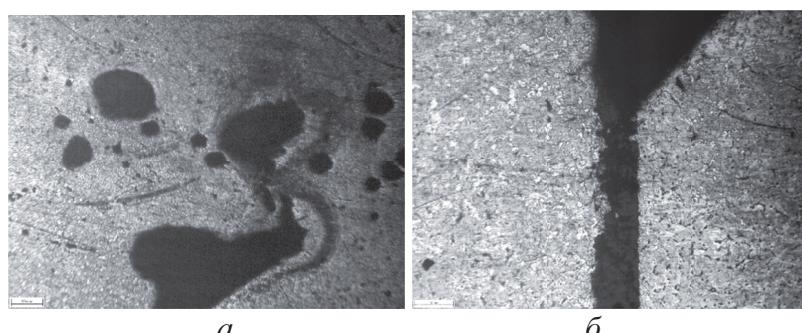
Структура зоны TIG сварки при силе тока 65А (x10):
